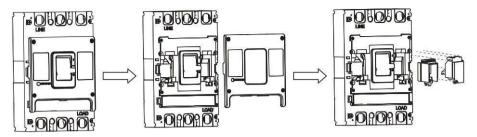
Схема установки аксессуаров внутрь корпуса аппарата
